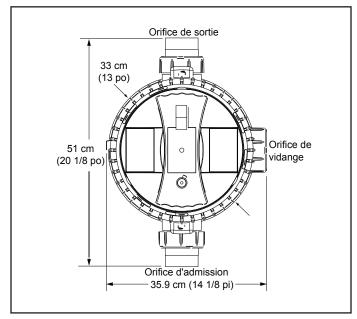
Dimensions, Filtre à cartouche série CS - Vue supérieure
